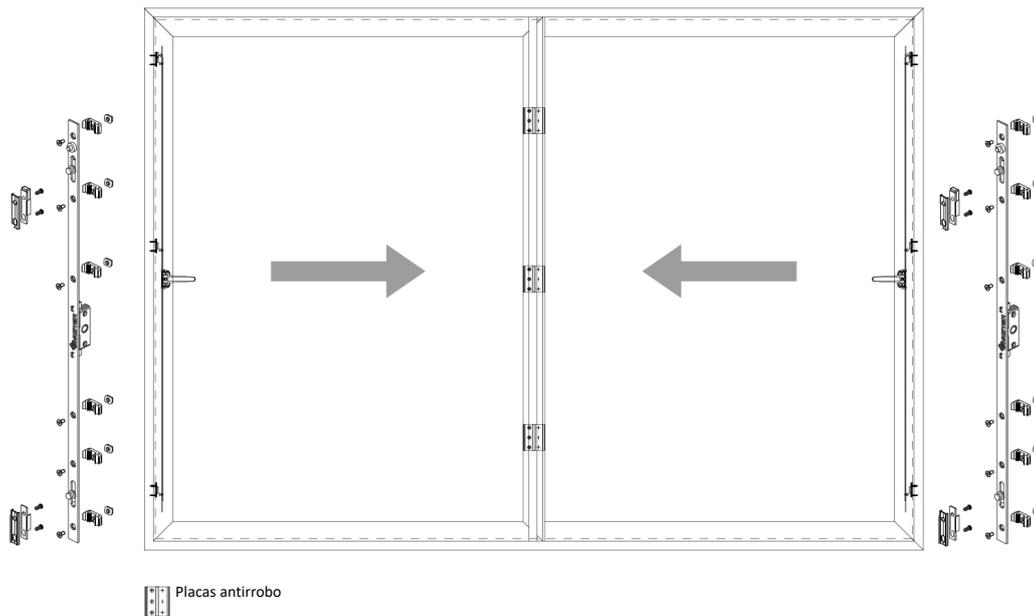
CONFIGURACIÓN DE CIERRES TIPO CORREDIZO RC2/RC3
